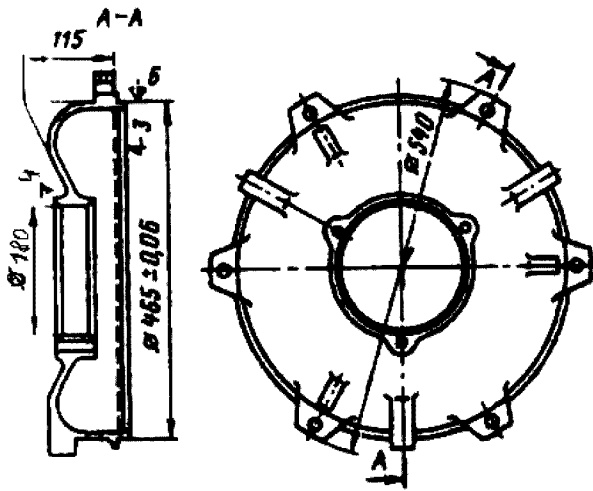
Подшипниковый щит асинхронного двигателя
